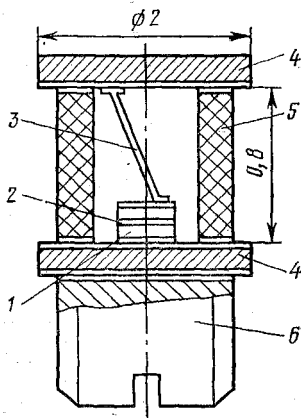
Устройство одного из типовых корпусов ЛПД для частот до 18 ГГц (все соединяемые поверхности металлизированы под пайку): 1 — основание для крепления структуры; 2 — полупроводниковая структура; 3 — соединитель; 4 — коваровый диск; 5 — керамический цилиндр; 6 — медный штифт с резьбой
